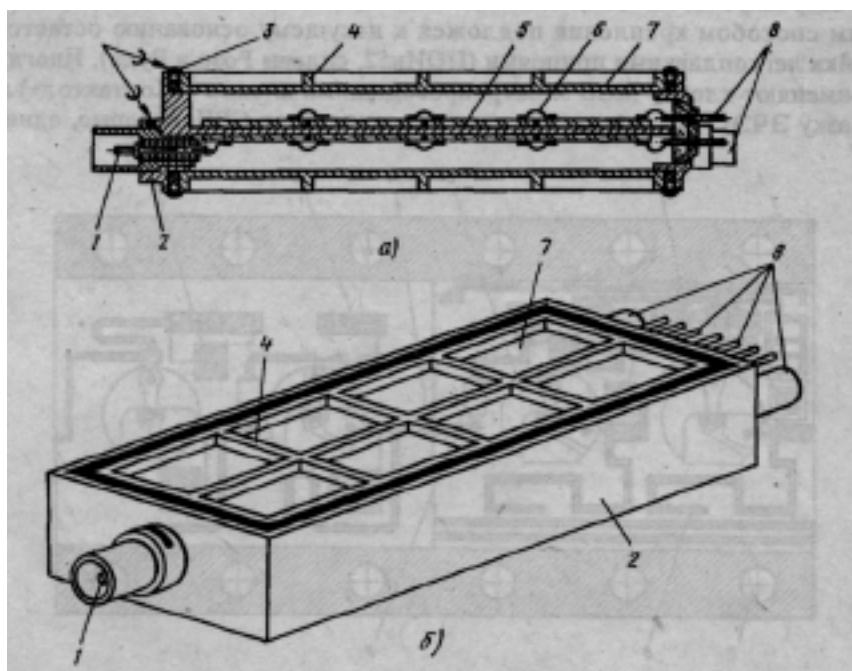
Конструкция модуля СВЧ: *a* — разрез конструкции; *б* — изометрия конструкции; 1 — высокочастотный разъем; 2 — каркас-основание; 3 — паяный шов; 4 — ребро крышки; 5 — планка каркаса; 6 — соединительная перемычка; 7 — крышка; 8 — комбинированный разъем
